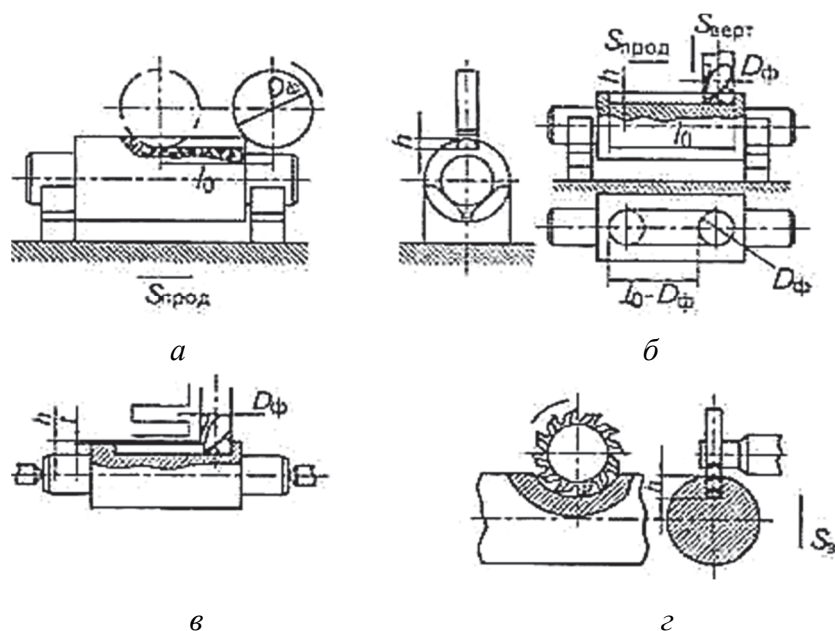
Схемы фрезерования на валах шпоночных канавок: *а* – дисковой фрезой; *б* – пальцевой фрезой; *в* – пальцевой двухперой фрезой; *г* – дисковой фрезой с вертикальной подачей;  $D_{\phi}$  – диаметр фрезы;  $l_o$  – длина канавки
